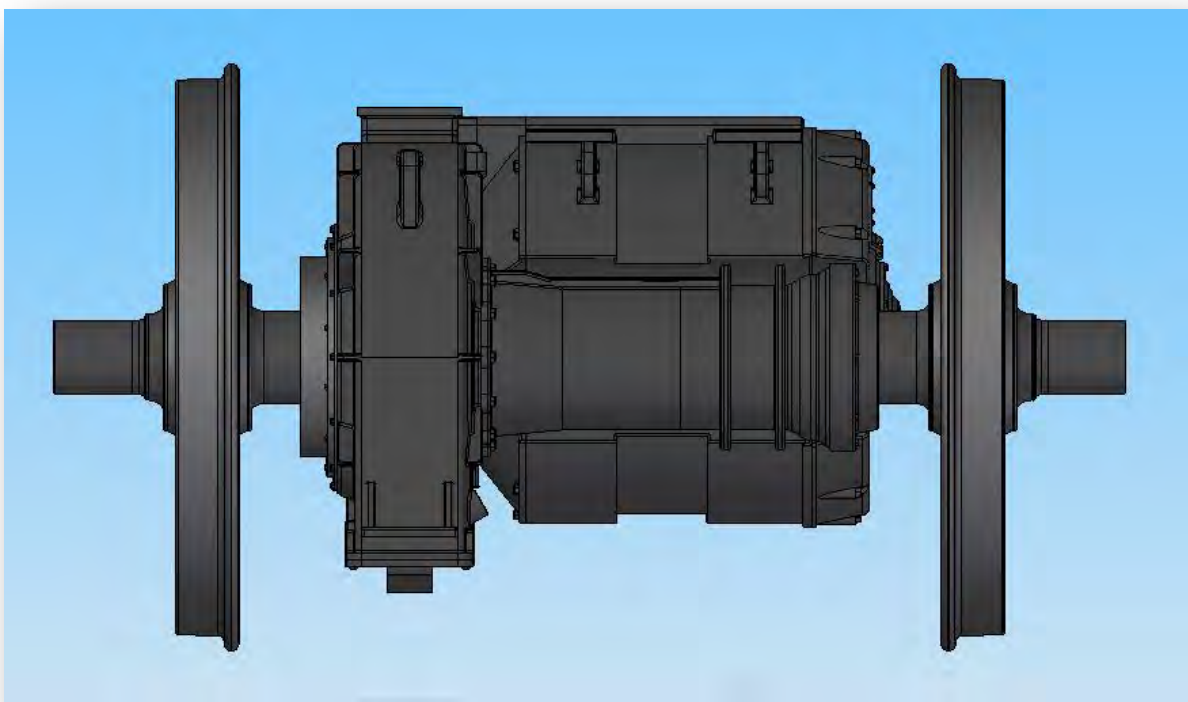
Vista en alzado del conjunto motor-eje montado.
